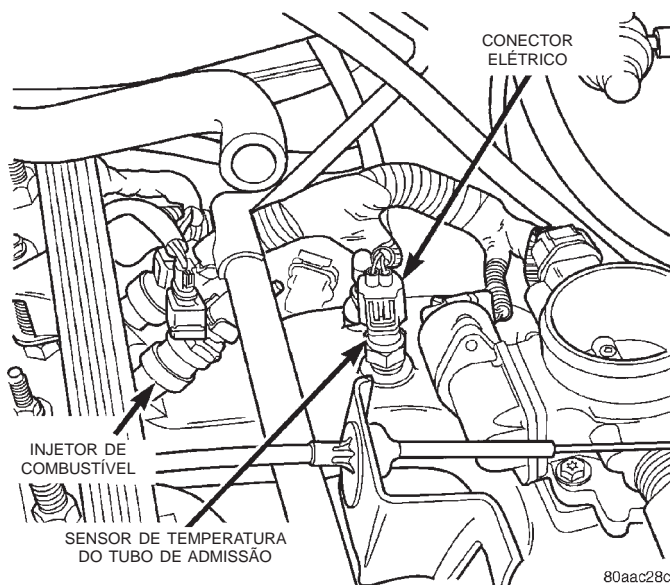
Localização do Sensor de IAT—Motor 2.5L
